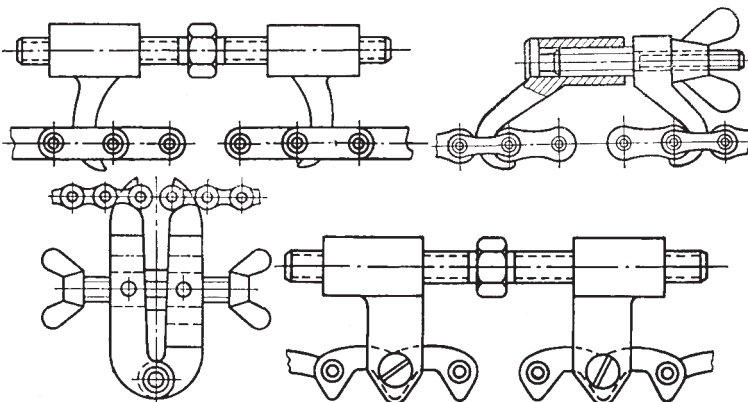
Приспособления для соединения звеньев втулочно-роликовой и зубчатой цепи
